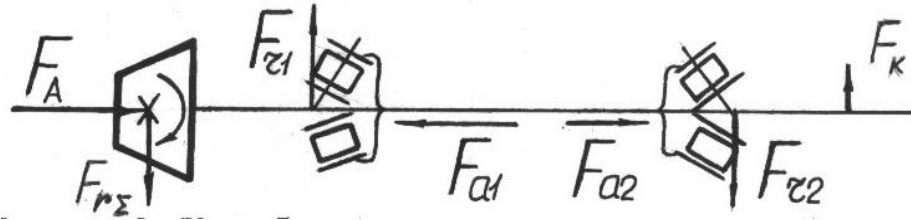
К подбору подшипника вала конической шестерни
